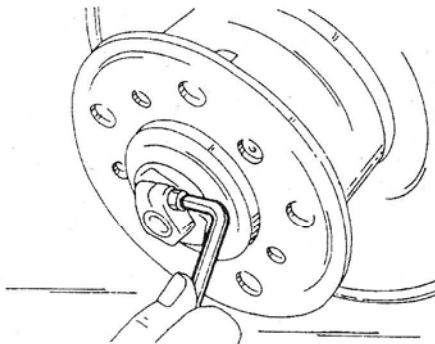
Крепление стяжной гайки для регулировки люфта колесных подшипников ослабляется ключом для болтов с внутренним шестигранником.
